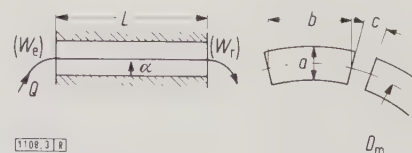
Kühlkanäle mit rechteckigem Querschnitt.
